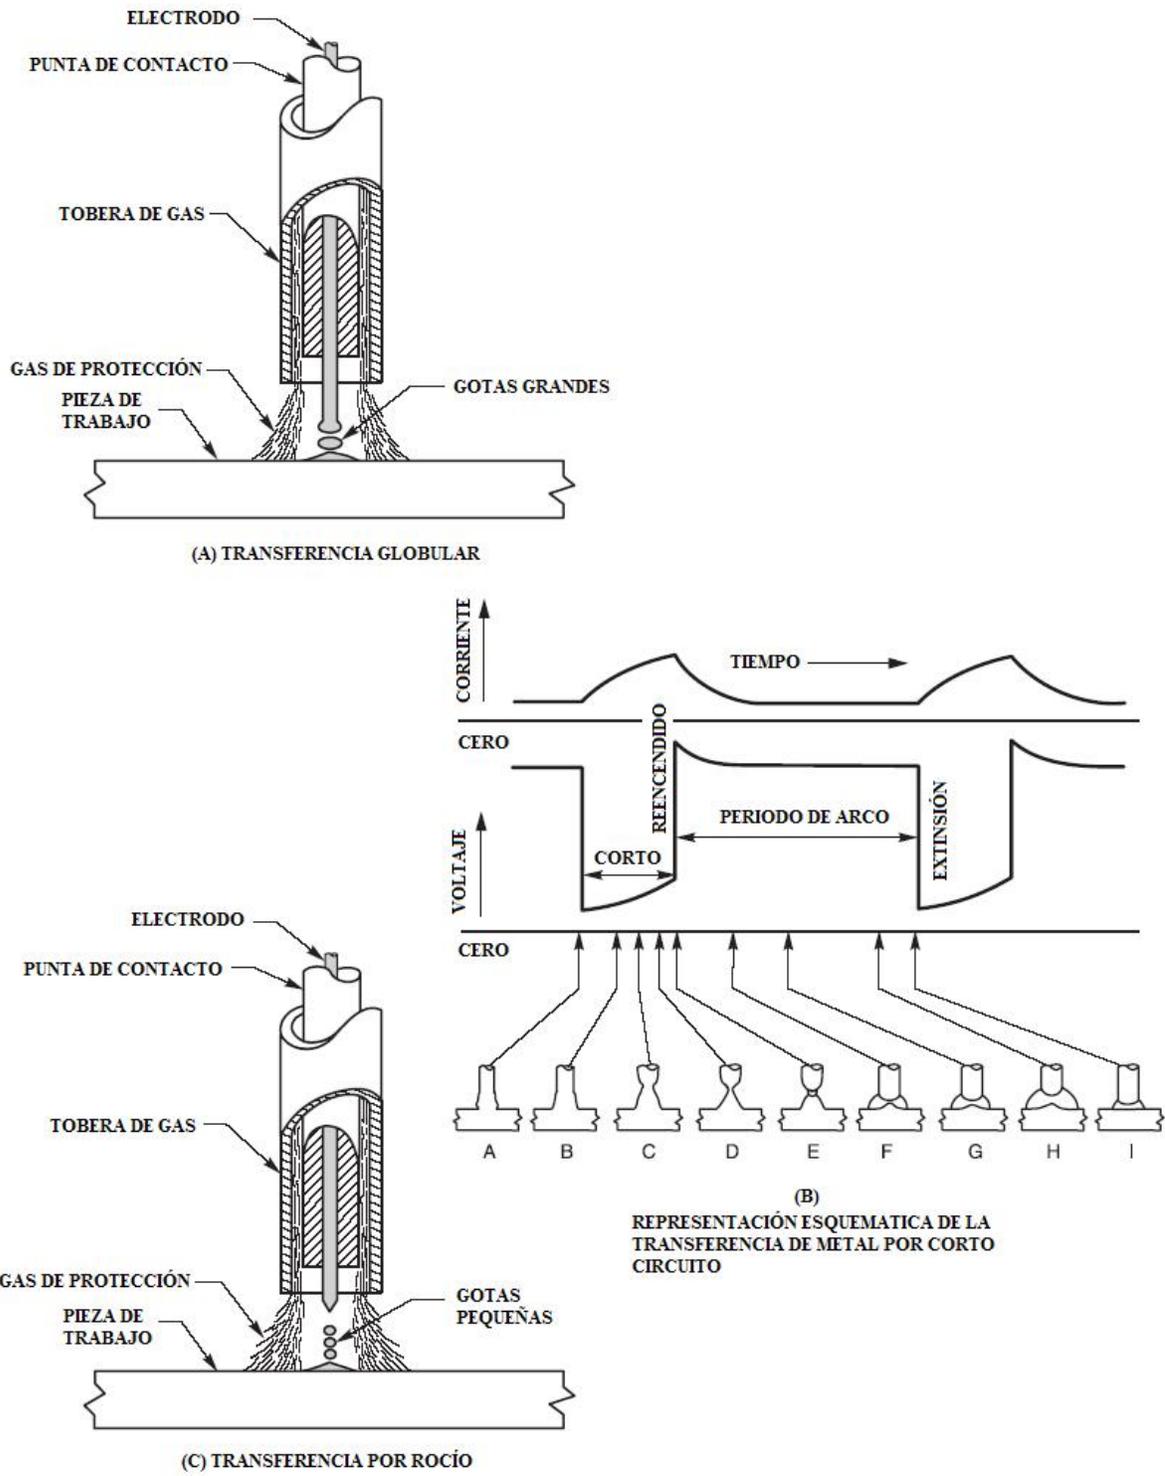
Transferencia Metálica en Soldadura por Arco Metálico Protegido con Gas
